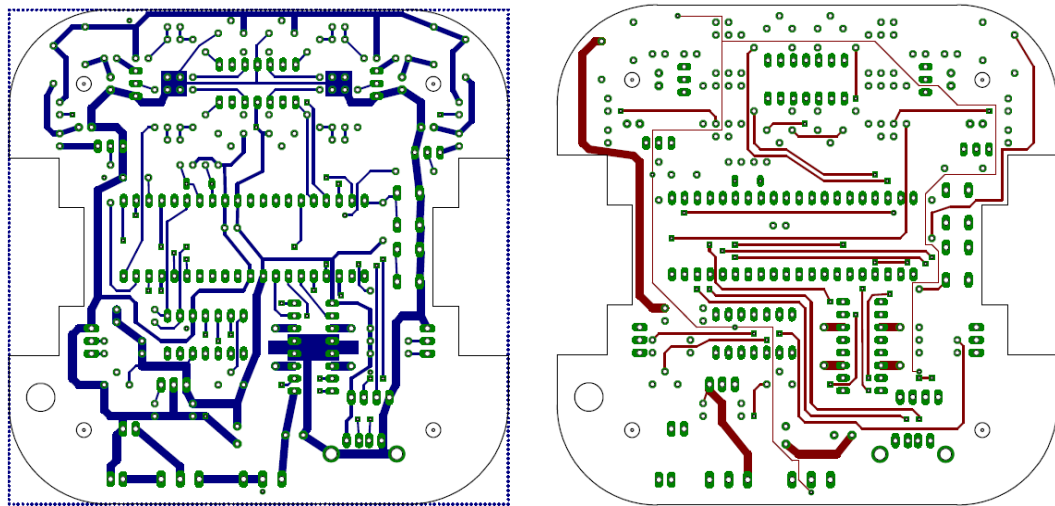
Capas inferior y superior de la placa PCB del robot
